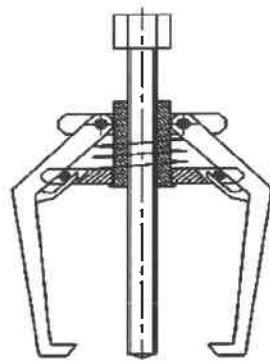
Вид предлагаемой конструкции съемного приспособления
